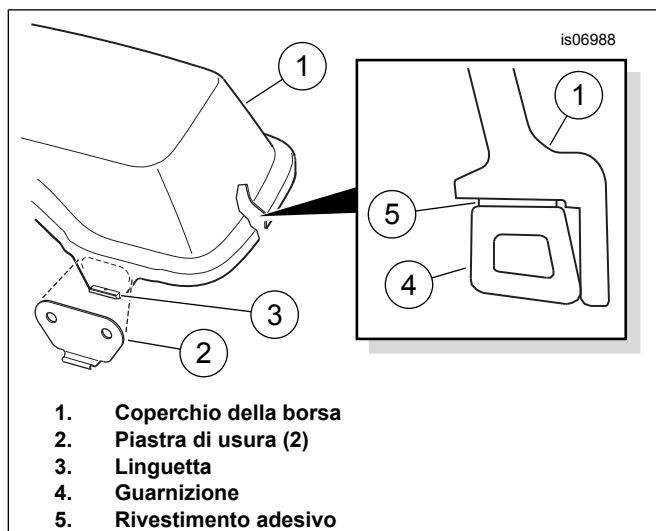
Assemblare le piastre di usura e la guarnizione sul coperchio della borsa
